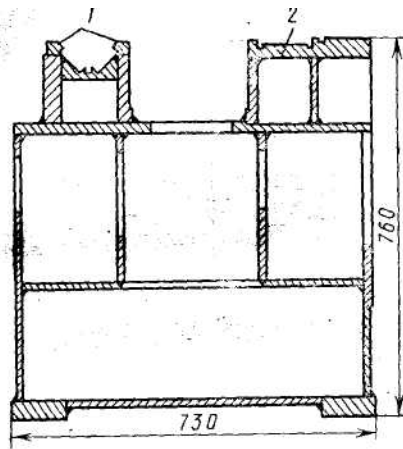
Розріз зварної станини шліфувального верстата
